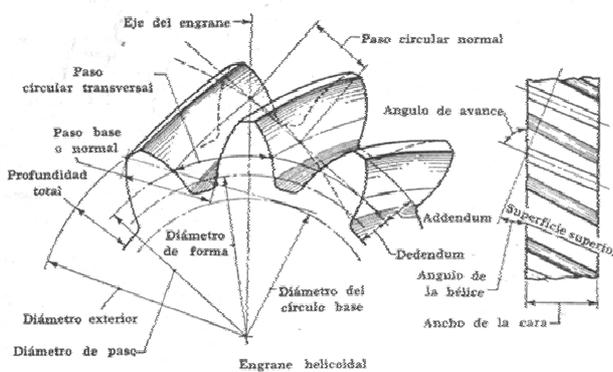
Geometría y parámetros de diseño del engrane helicoidal.
